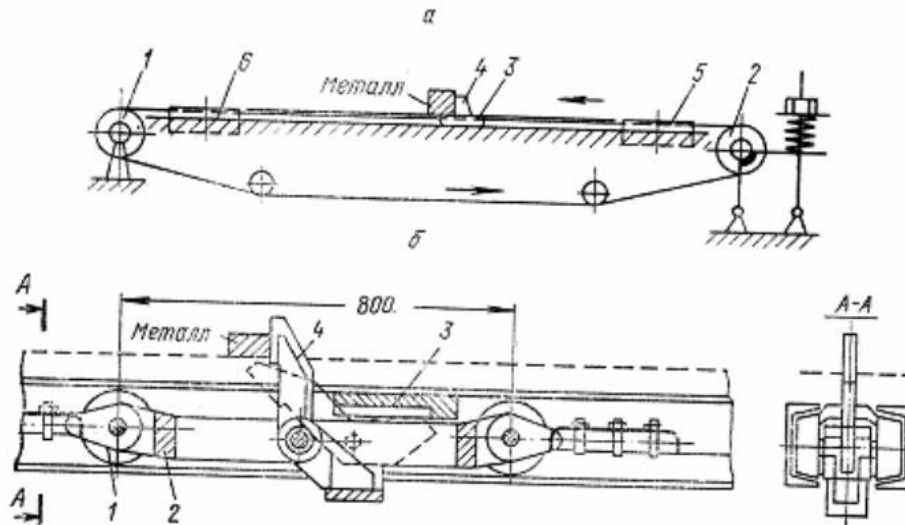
Канатний шлеппер: а - загальний вигляд: 1 - приводний барабан; 2 - натяжний блок; 3 - візок; 4 - упорний палець; 5,6 - рольганги; б - конструкція візка: 1 - ковзанка; 2 - корпус; 3 - упор
